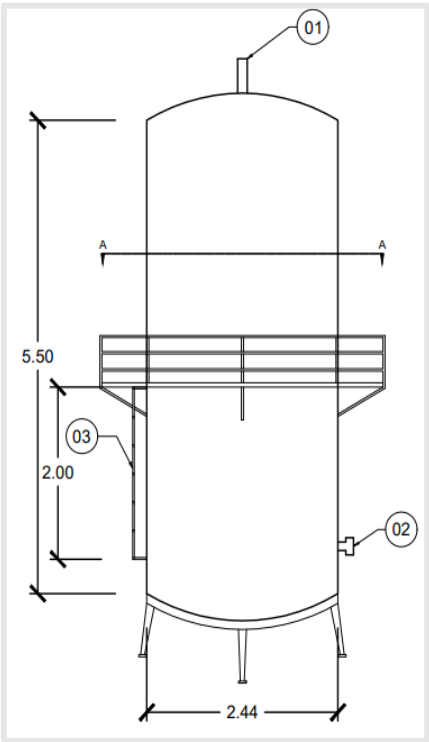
Plano correspondiente a vista lateral de la columna de destilación.
